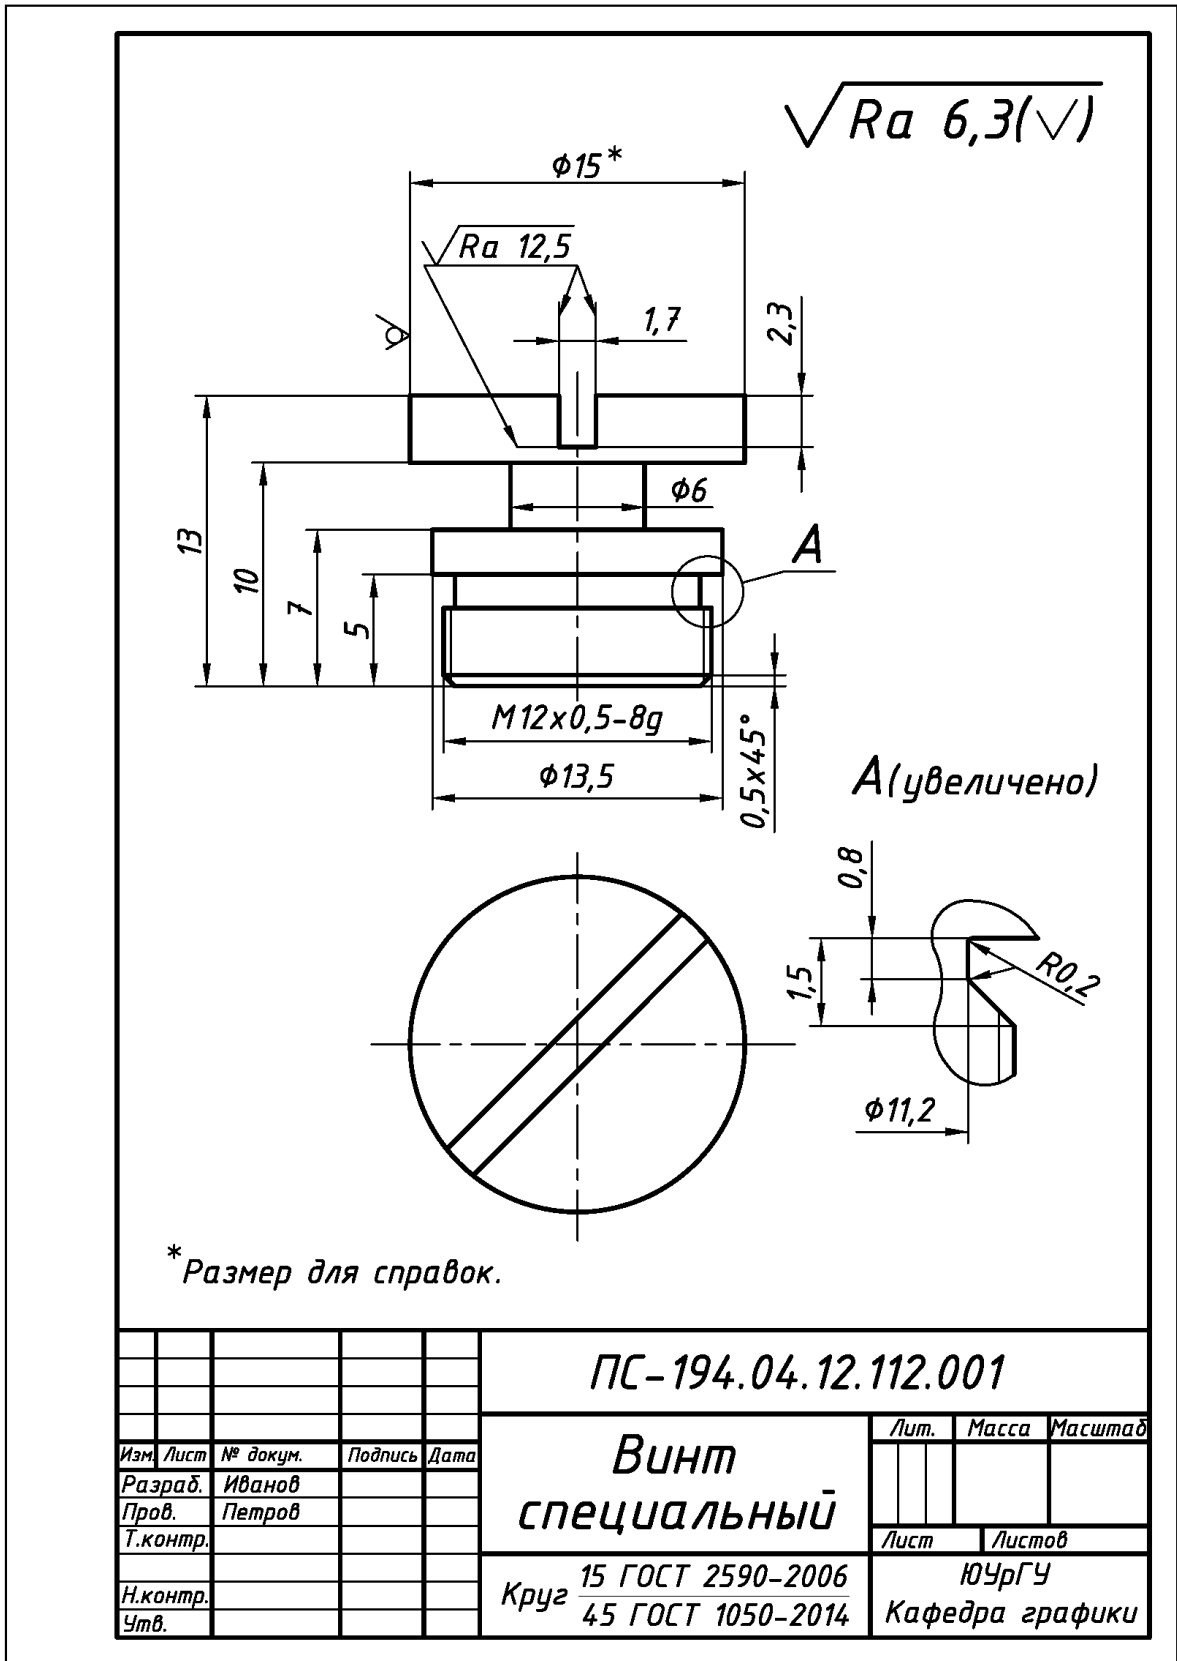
Пример выполнения и оформления эскиза детали «Винт специальный», изготовленной из металла токарно-фрезерной обработкой
